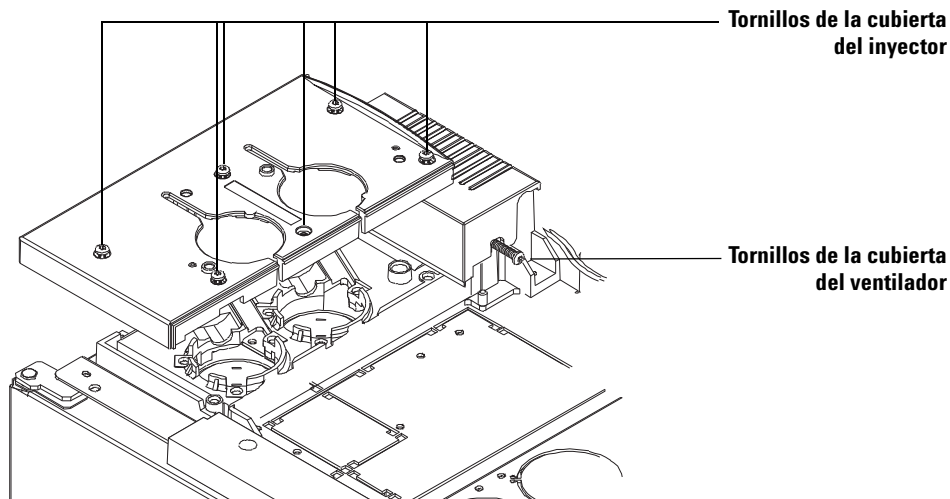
Extracción de la cubierta superior del puerto de inyección y de la cubierta del ventilador del inyector (GC serie 6890)
